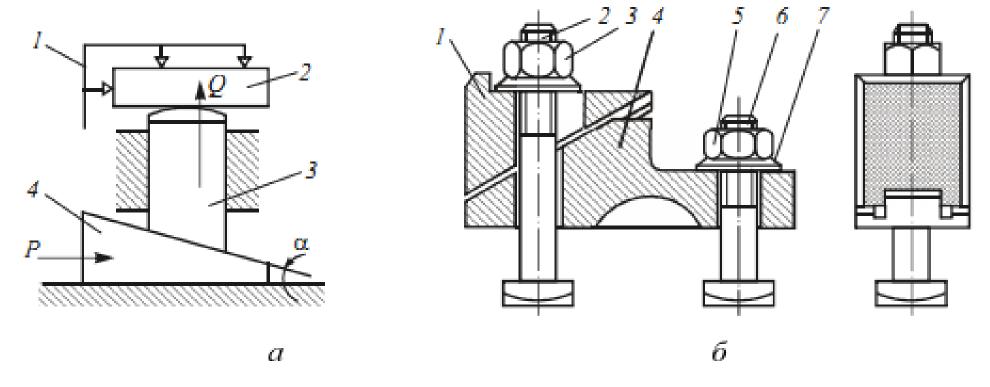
Схема (a) и конструкция (б) клинового зажимного механизма
